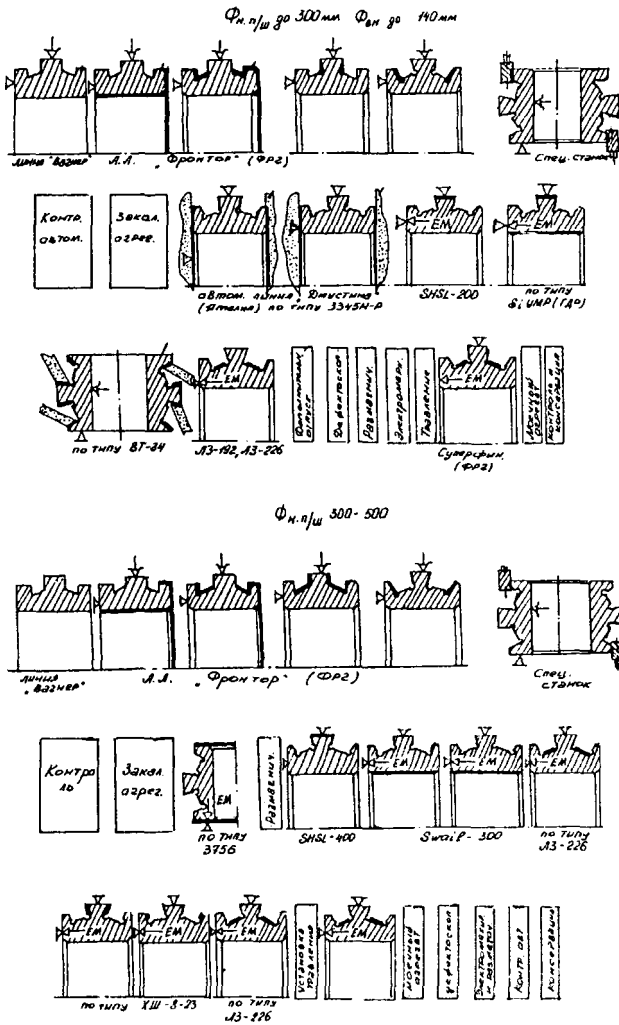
Перспективный процесс механической обработки внутренних колец роликовых сферических подшипников
